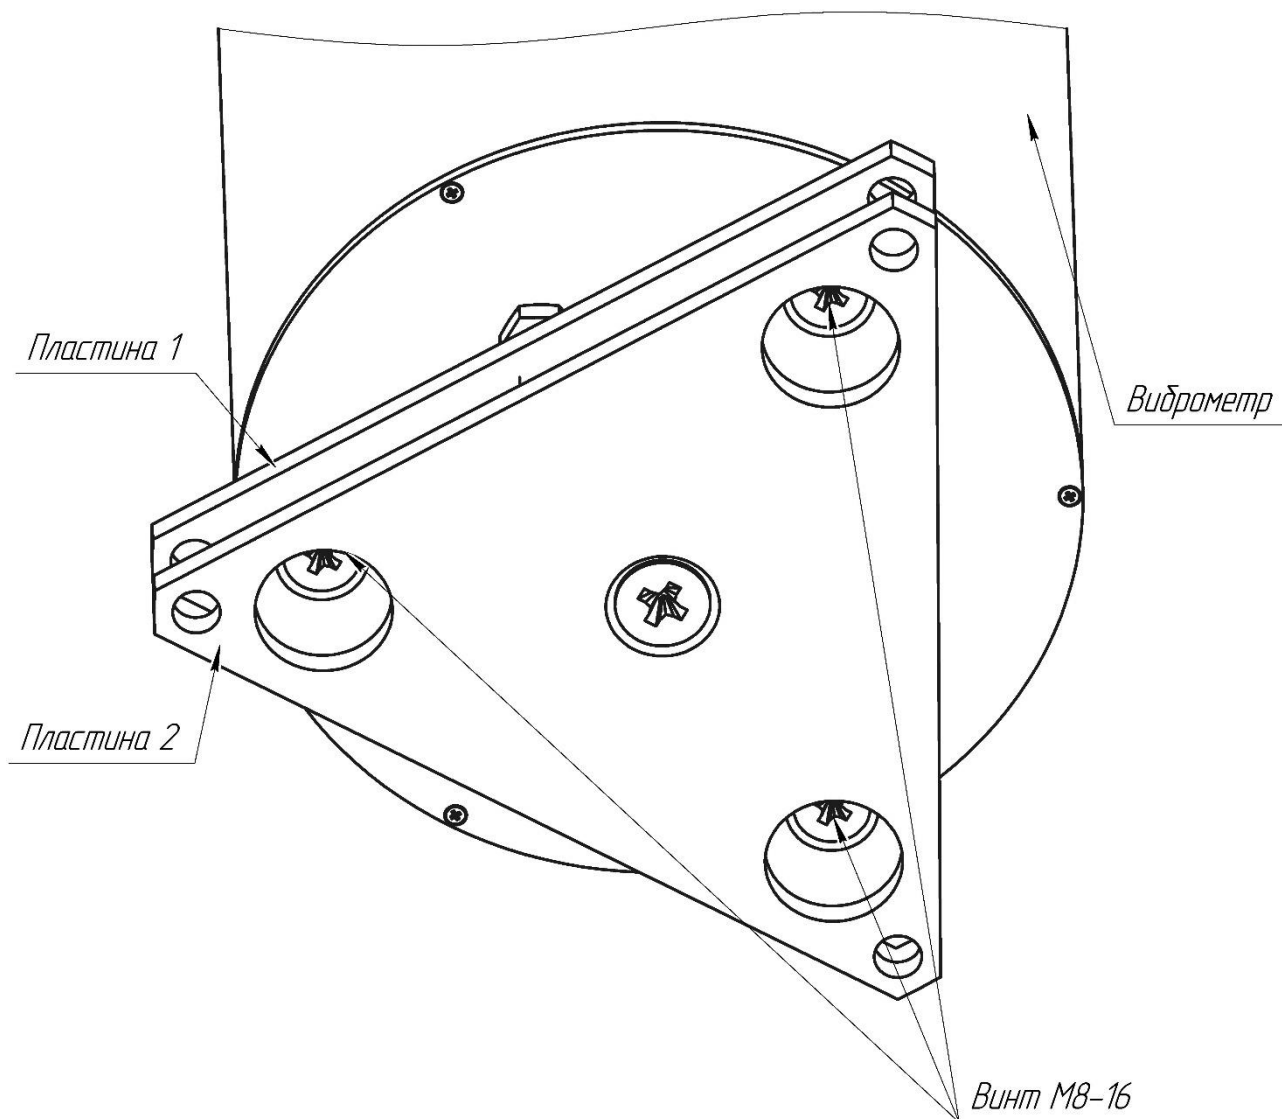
Крепление виброметра с регулировкой – Шаг 2
